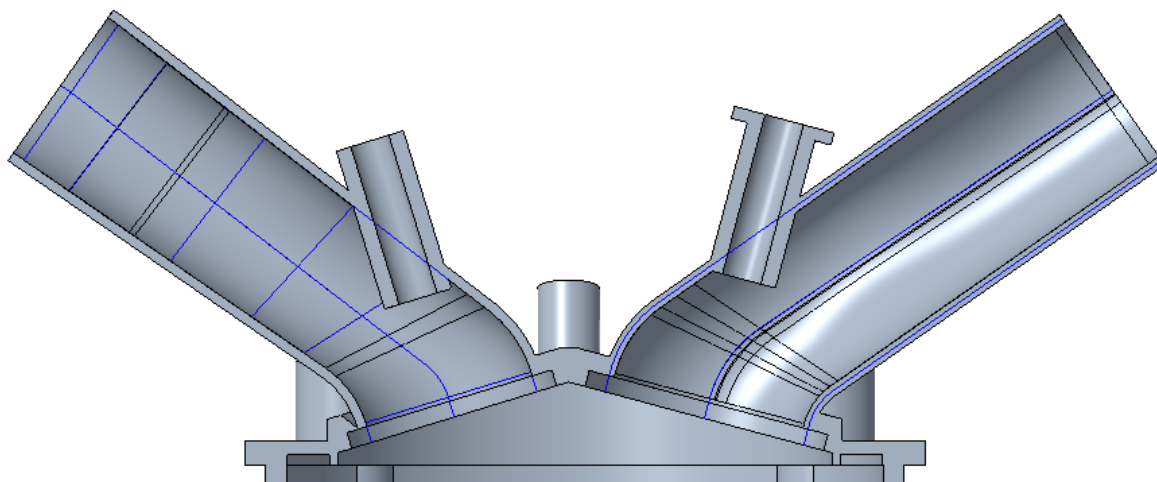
Zobrazenie spliny prechádzajúcej jednotlivými bodmi
